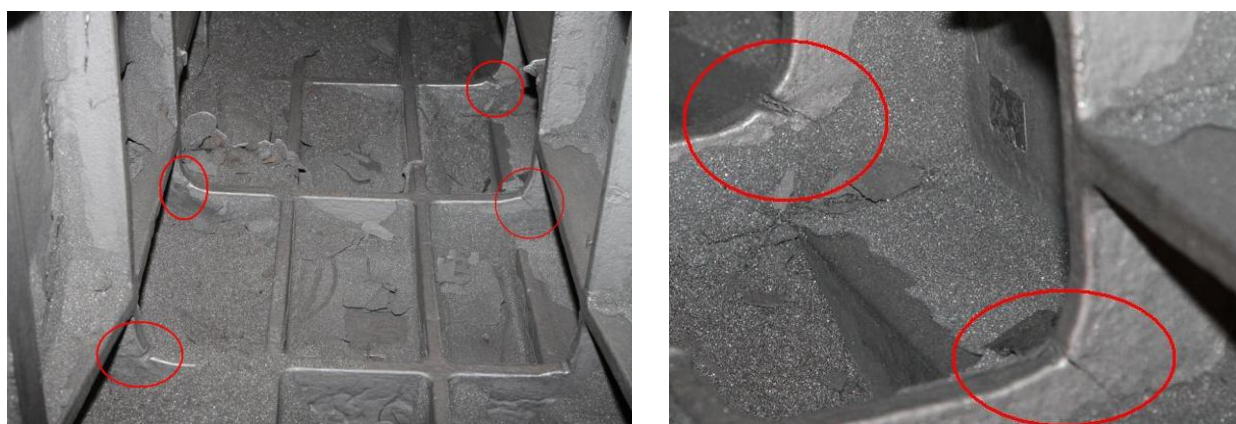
Трещины, образующиеся на внутренних ребрах жестки отливки «Колонна»
